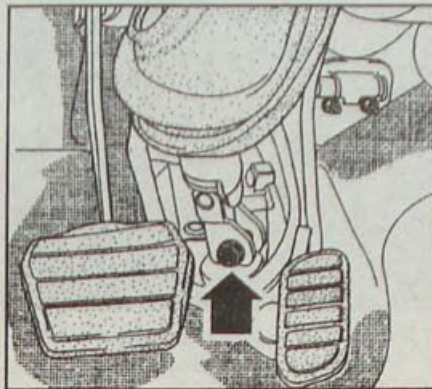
Расположение гайки и болта крепления карданного шарнира рулевого вала к рулевой передаче
